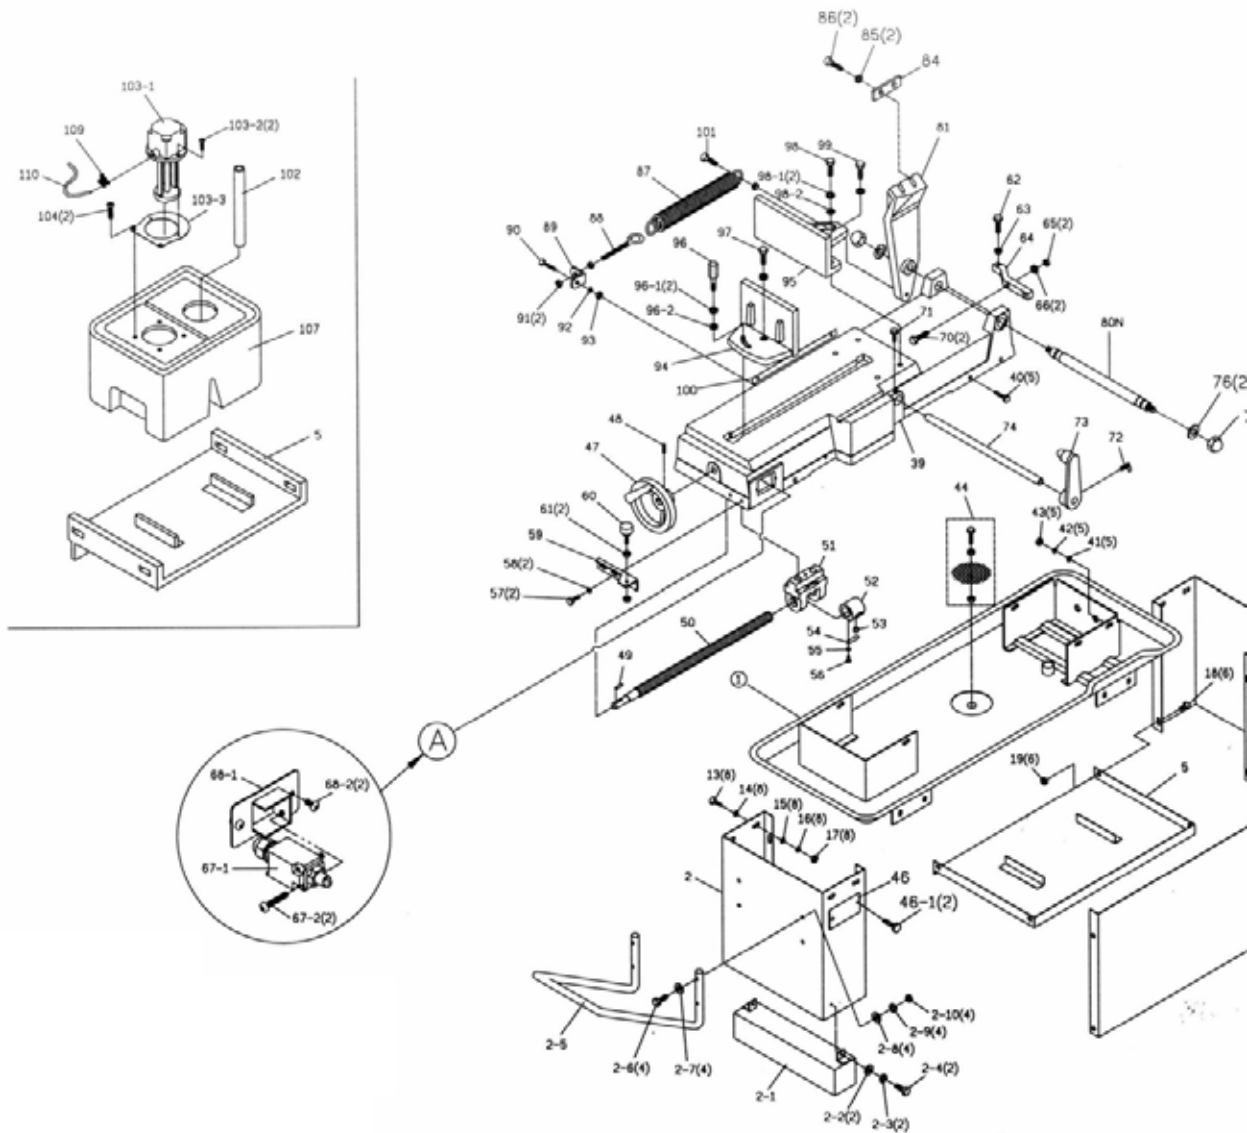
Explosionszeichnung 1 - Explosion drawing 1 S181
